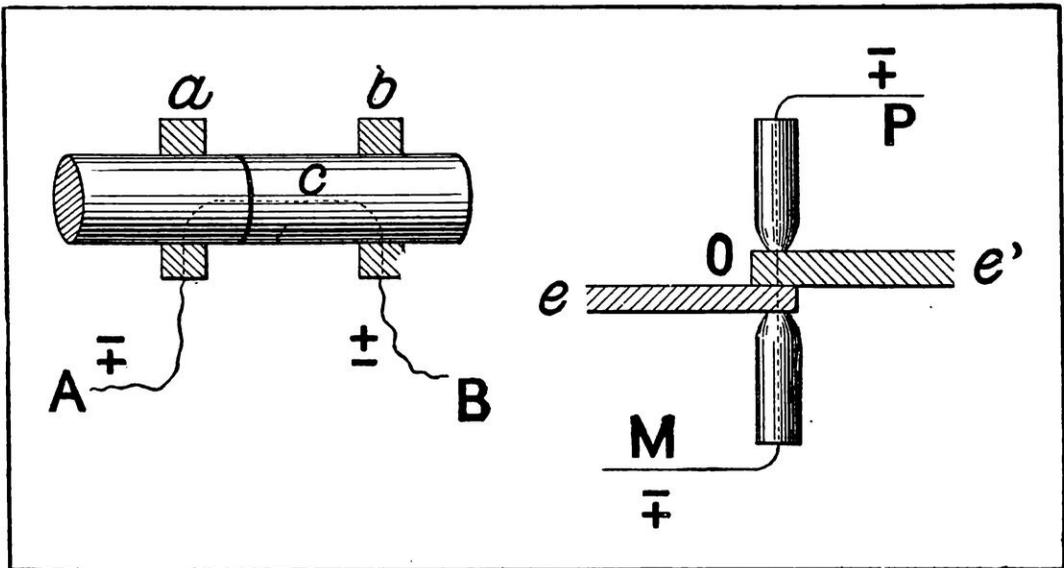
ET 2. — LE PROCÉDÉ DE SOUDURE ÉLECTRIQUE PAR COURT-CIRCUIT
